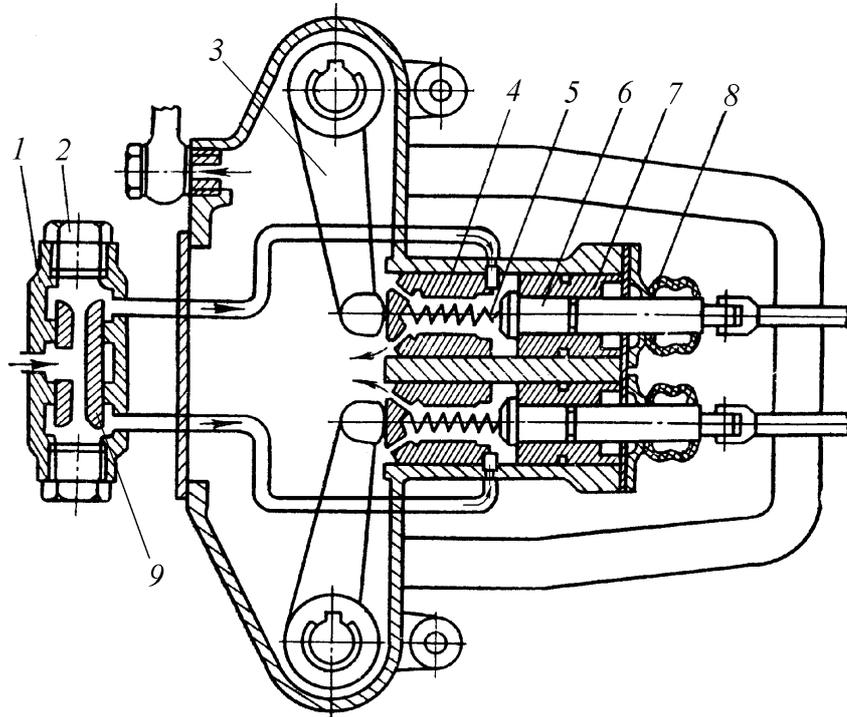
Схема гидравлического сервопривода управления бортовыми фрикционами трактора Т-130: 1 – корпус делителя потока; 2 – пробка канала золотника; 3 – поворотный рычаг; 4 – поршень; 5 – пружина; 6 – толкатель; 7 – втулка толкателя; 8 – защитный чехол; 9 – золотник
